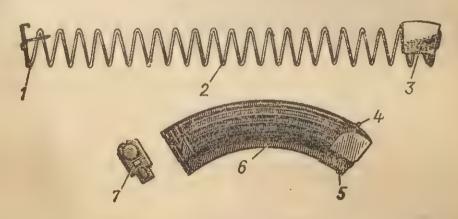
Коробчатый магазин: 1— стопорная планка; 2— пружина; 3— подаватель; 4— опорный выступ; 5— зацеп; 6— корпус; 7— крышка
